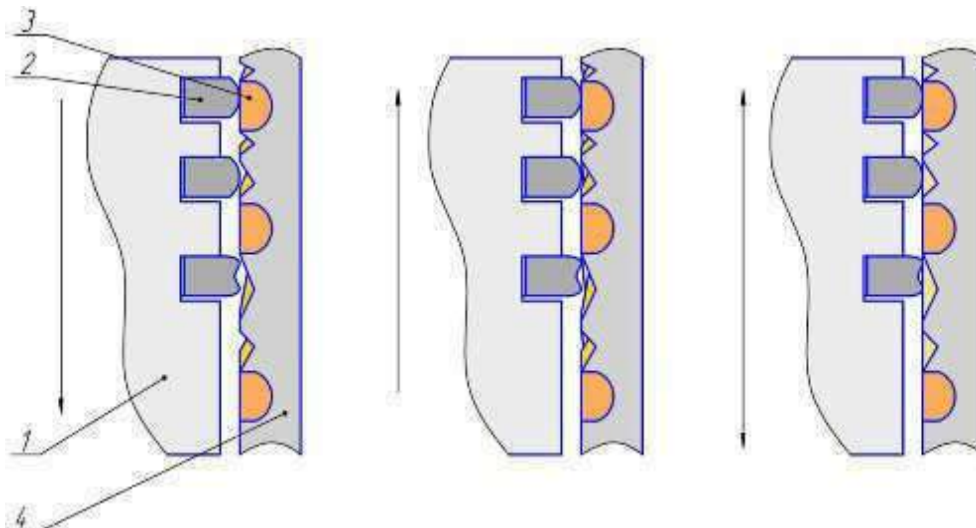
Схема формування плівки кольорового металу на поверхні гільзи циліндрів: 1 – поршень; 2 – поршневе кільце; 3 – канавки; 4 – гільза циліндрів
